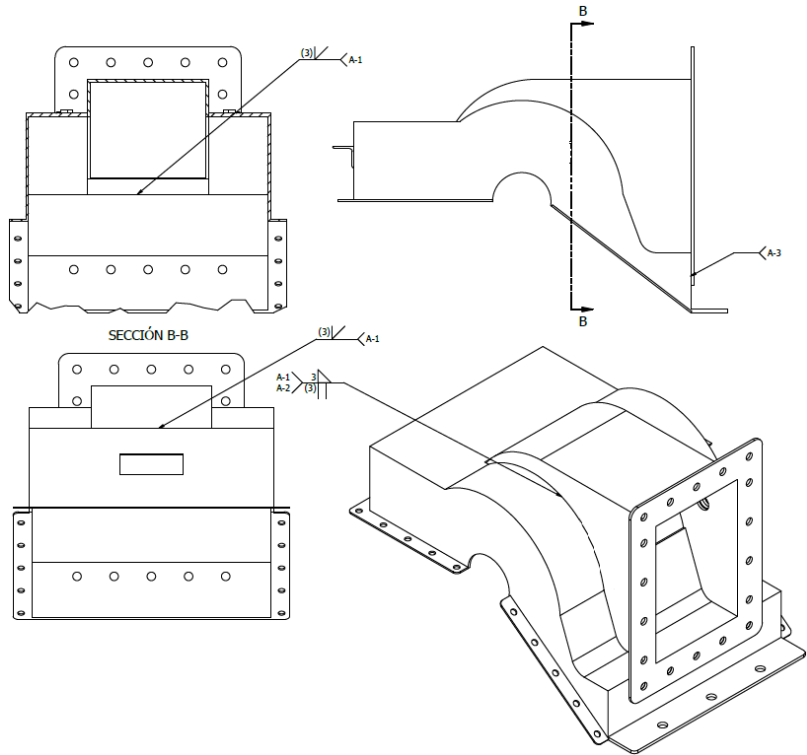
Plano de ensamble soldado: Carcasa superior completa.
